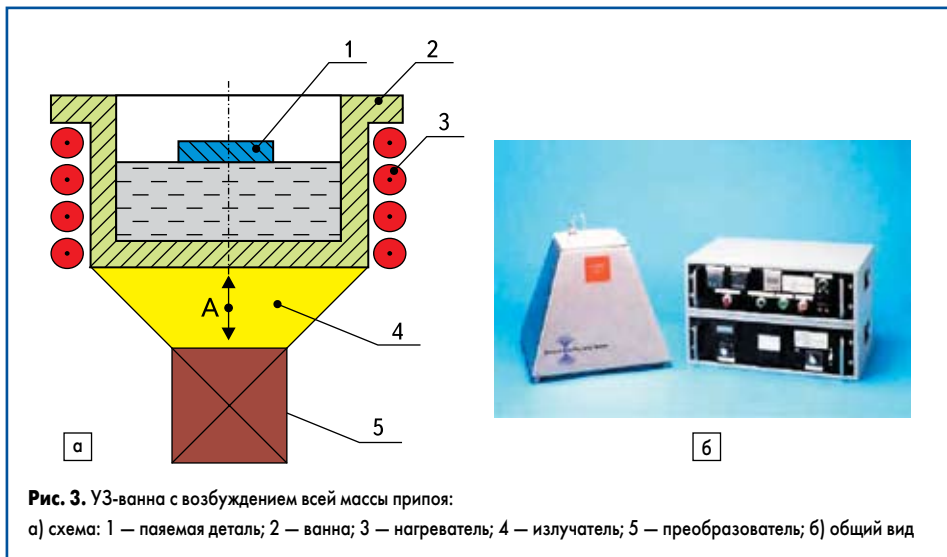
УЗ-ванна с возбуждением всей массы припоя: а) схема: 1 — паяемая деталь; 2 — ванна; 3 — нагреватель; 4 — излучатель; 5 — преобразователь; б) общий вид
